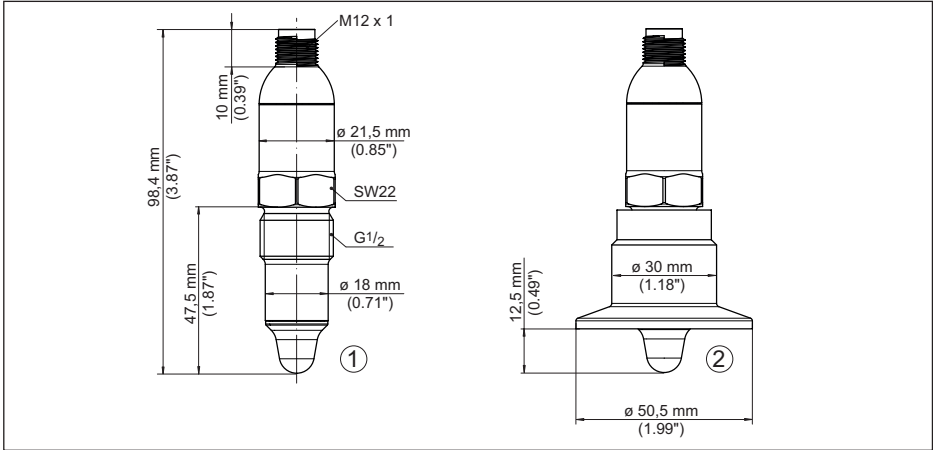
VEGAPOINT 11, Hygieneausführung - Gewinde
